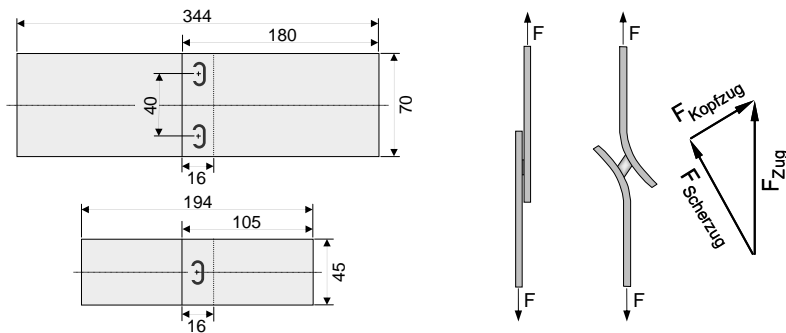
Ein- und Doppelpunkt-Scherzugprobe mit Klammerschweißnähten; durch Verformung der Probe verursachte Mischbeanspruchung aus Kopf- und Scherzug.
